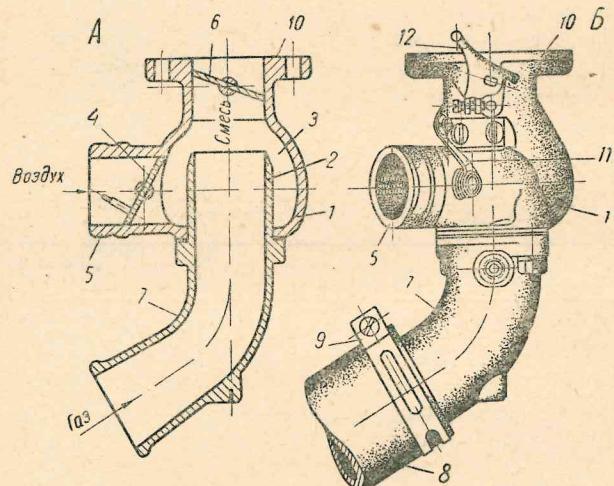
Разрез (слева) и общий вид (справа) смесителя газа с воздухом в автомобилях ГАЗ:
